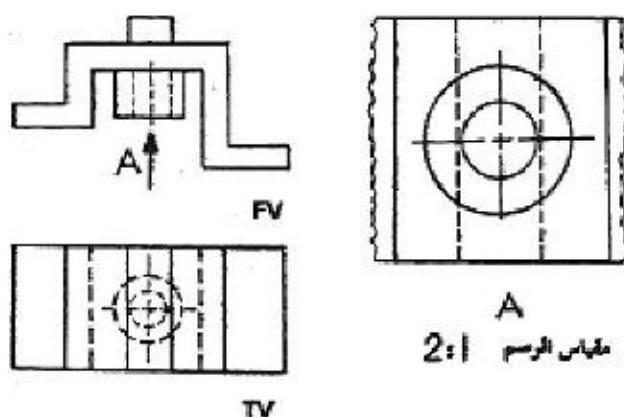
مسقط كامل مع نصف مسقط لتمثيل جسم ممتدا
